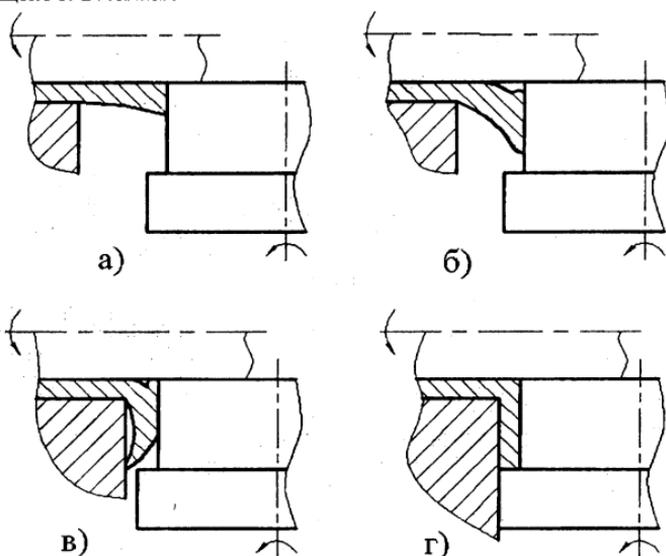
Стадии формообразования фланцев в трубных заготовках торцовой раскаткой
